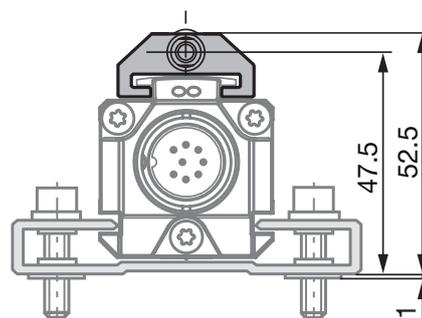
Dimensions et distances pour le capteur de position BTL5-T-2814-1S
